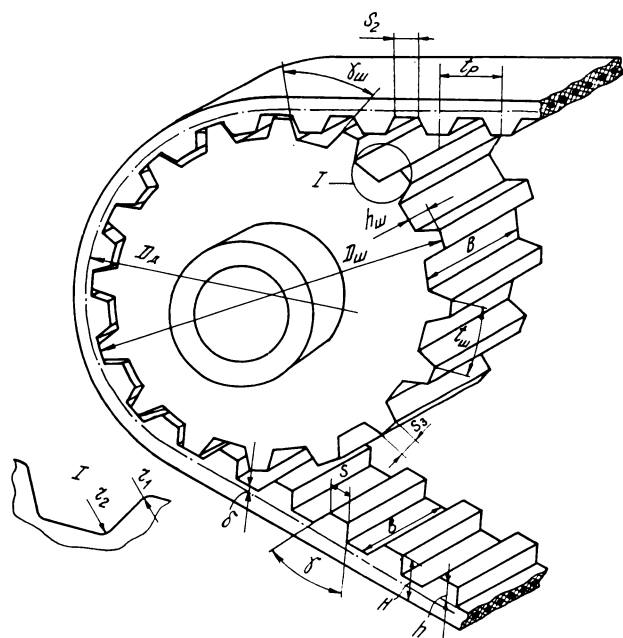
Обозначения элементов зацепления: для ремня: t_p — шаг зубьев; b — ширина; H — полная высота; h — высота зуба; γ — угол профиля зуба; S — толщина головки зуба; S_2 — размер впадины; для шкива: D_d — диаметр делительной окружности; $t_{ш}$ — шаг зубьев по дуге $D_{ш}$; $h_{ш}$ — высота зуба; S_2 — толщина головки зуба; B — ширина; $\gamma_{ш}$ — угол впадины; r_1 и r_2 — радиусы скругления зуба
